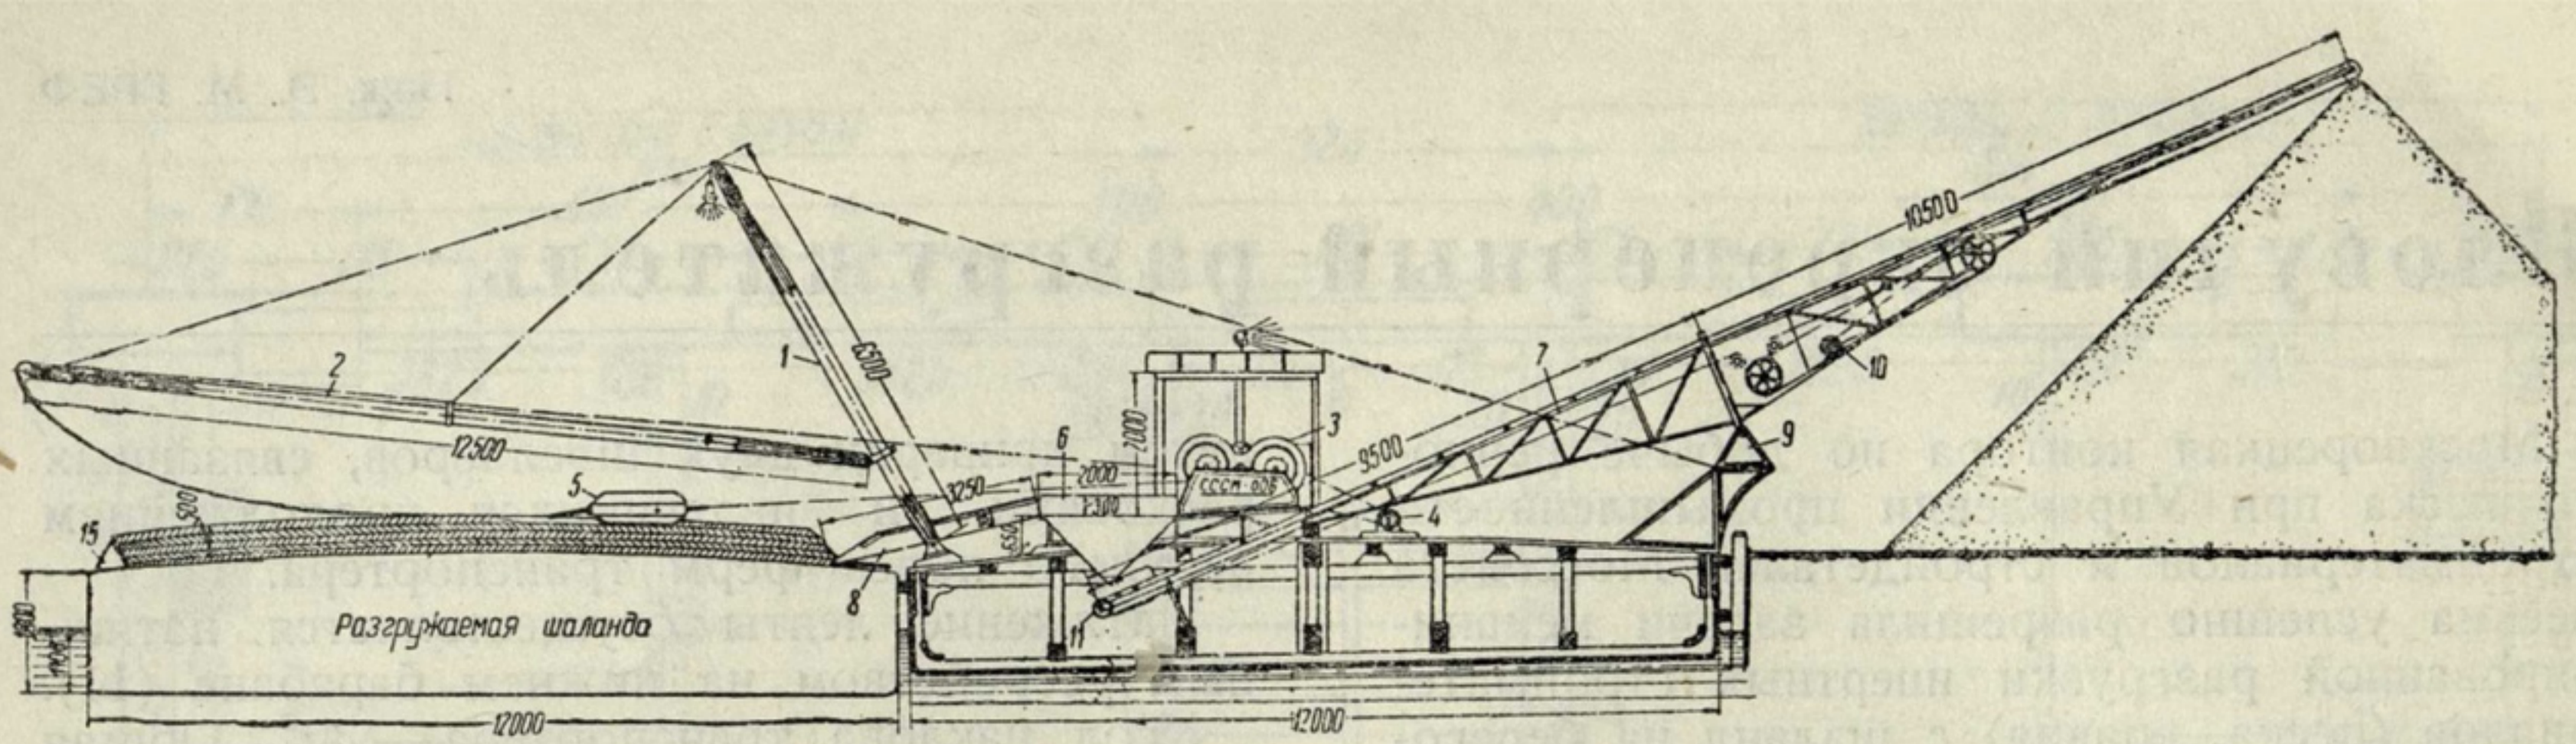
Скреперный разгрузатель. Поперечный разрез.
